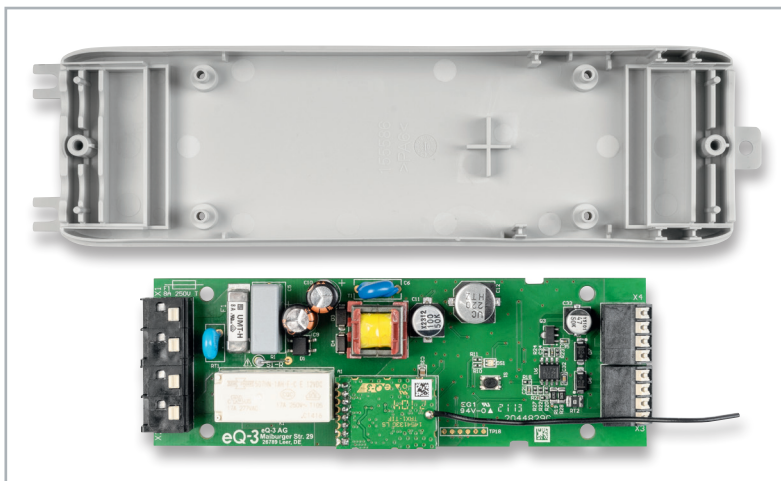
In dieser Ausrichtung wird die Platine in die Gehäuseunterschale gelegt.
